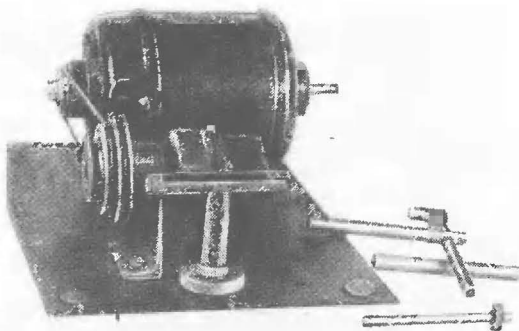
Внешний вид станка для изготовления и переточки металлических резцов.
